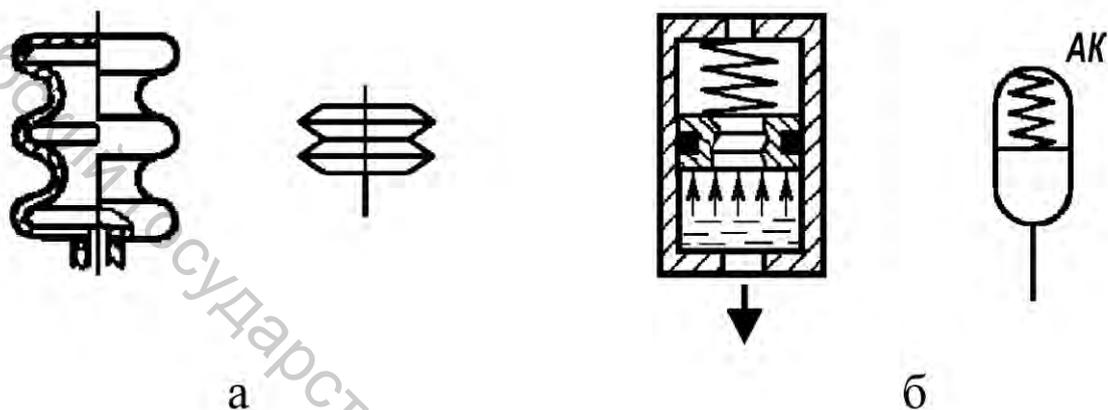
Гидроаккумуляторы: с упругим корпусом (сильфонный) (а) и пружинный (б)
